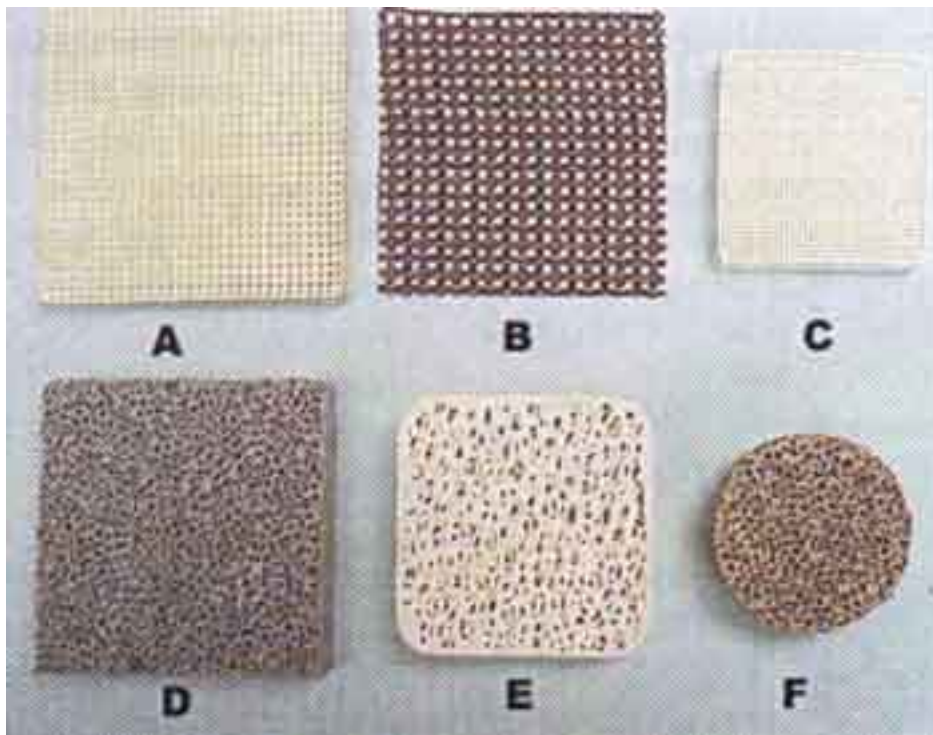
Шесть различных типов фильтров: А - 3,25 дюйма прессованный керамический фильтр (10
